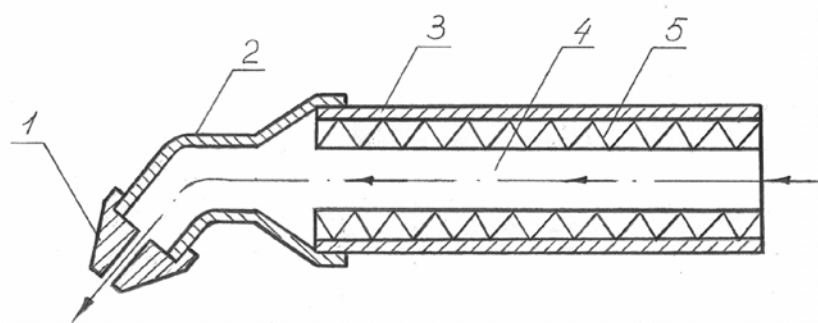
Схема электрической горелки для сварки пластмасс:
